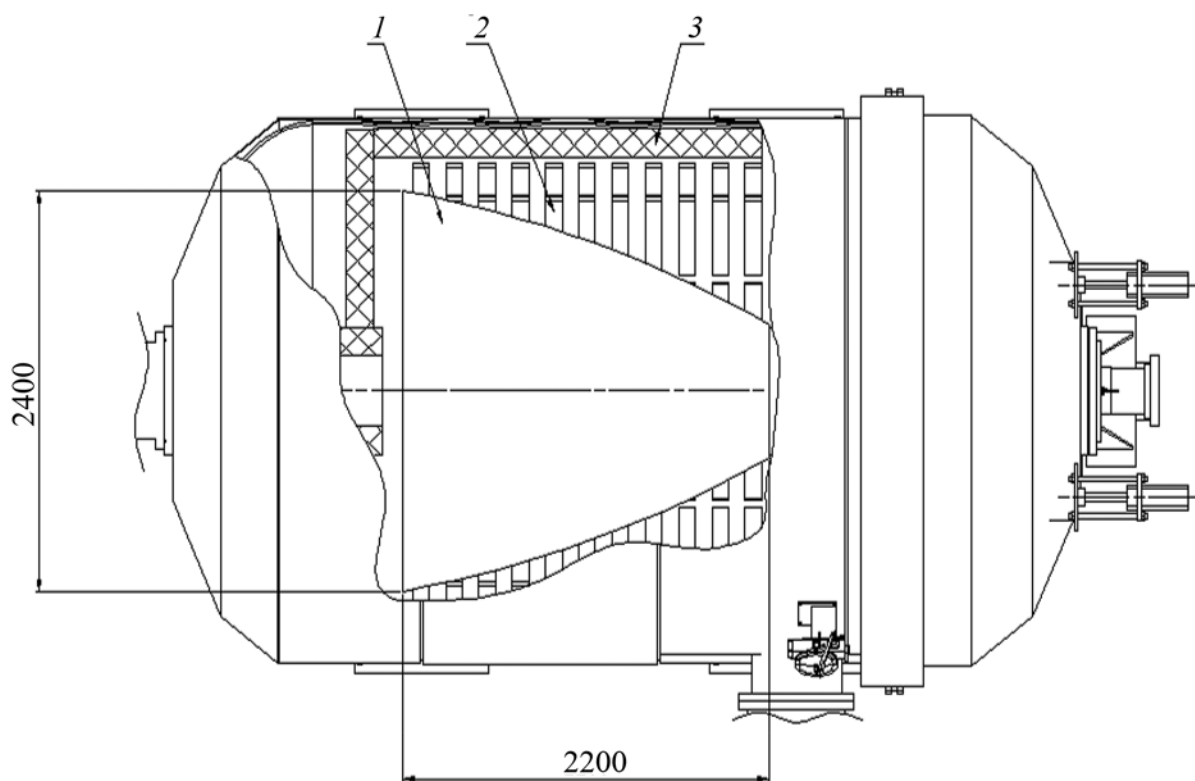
Конструкция вакуумно-компрессионной печи для нагрева под пайку:
